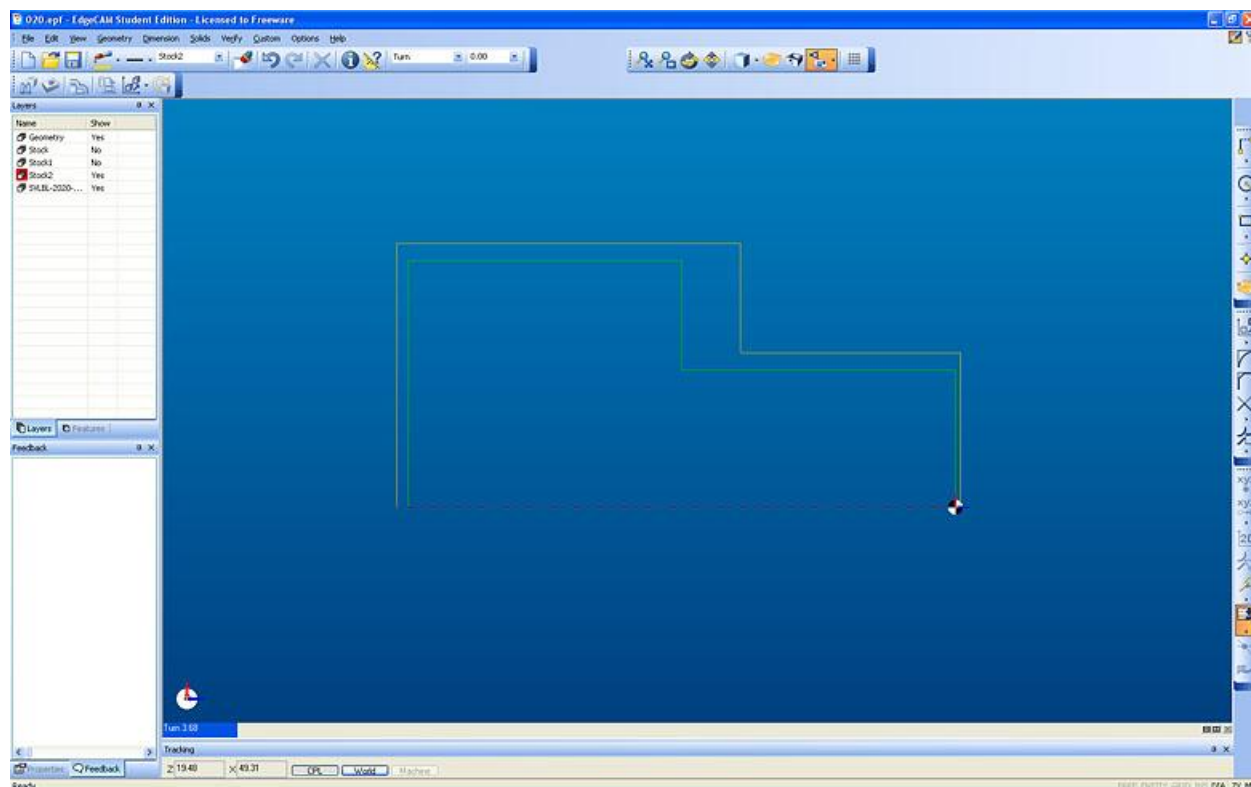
Edgcam. Создание заготовки для токарной обработки
